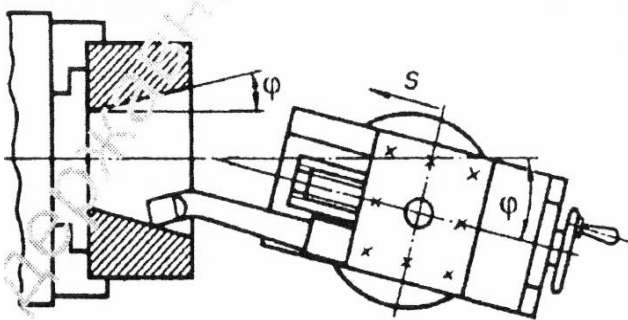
обробка конуса за допомогою повороту каретки верхнього супорта
